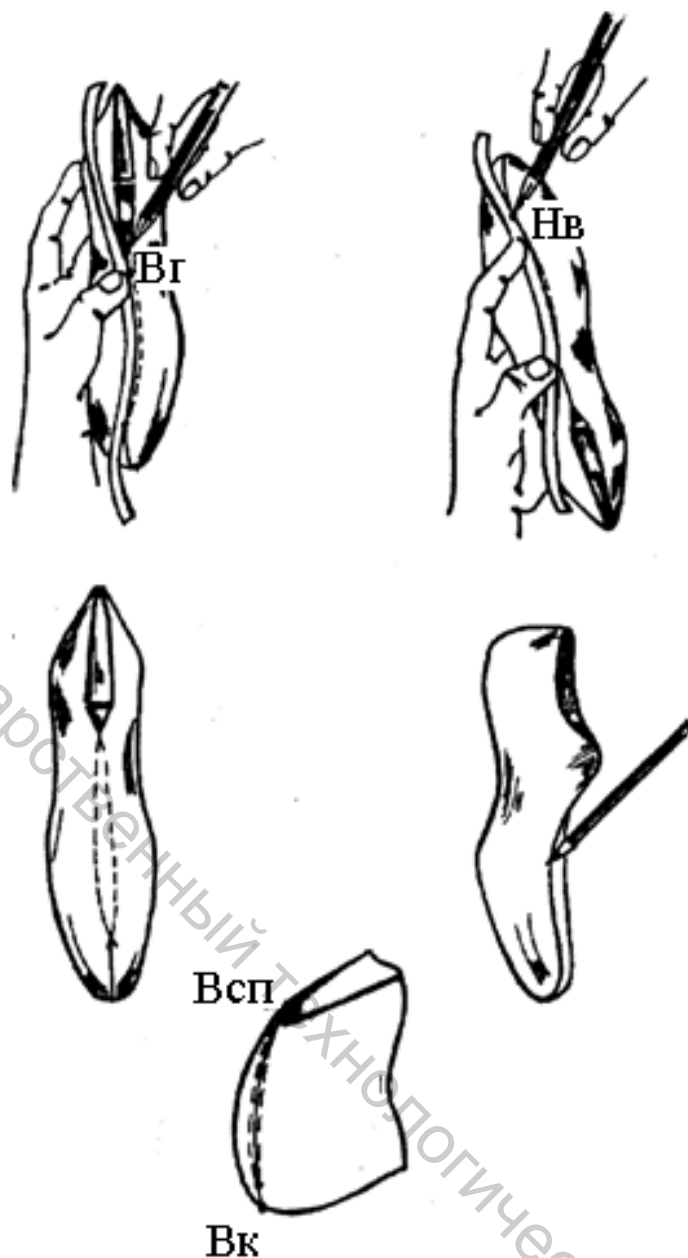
Этапы подготовки колодки к получению условной развертки боковой поверхности колодки
